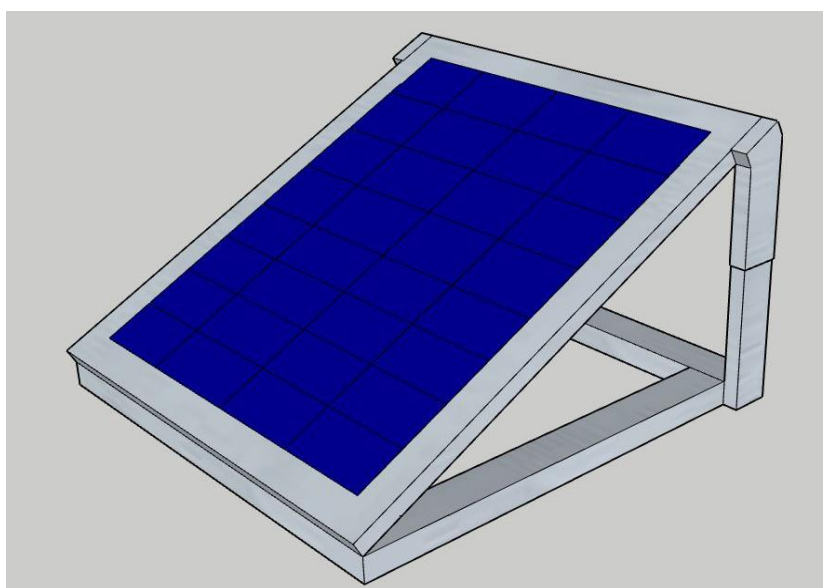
Painel solar de base fixa, o painel tem dimensões de 148 cm por 66 cm.
